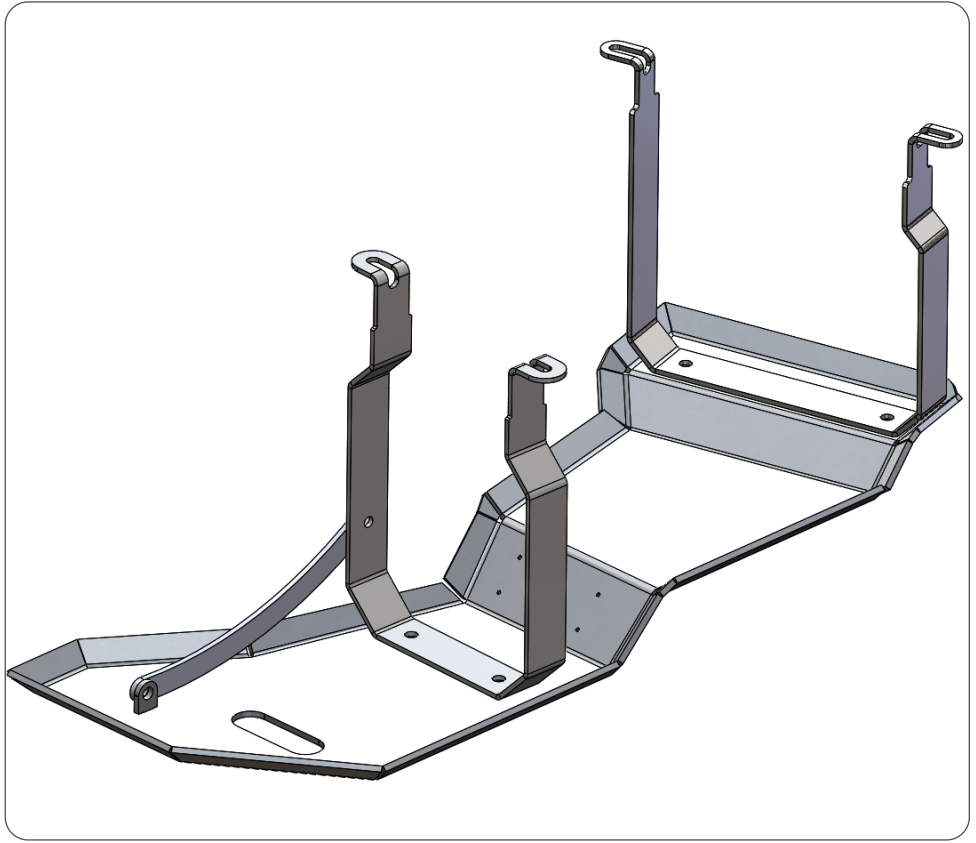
CAD Abbild des Unterfahrschutzes inkl. Halter/ CAD image of the skid plate including the brackets
